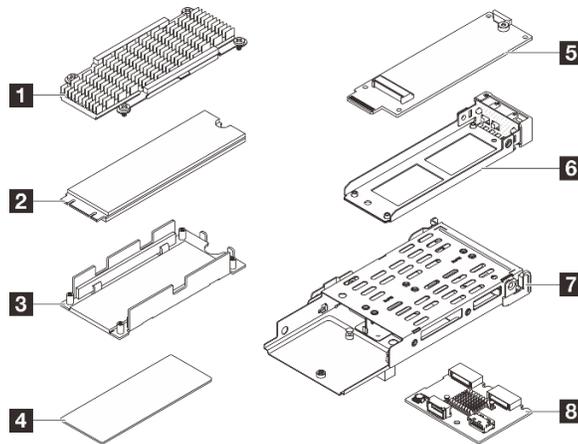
Teile einer hinteren M.2-Baugruppe
